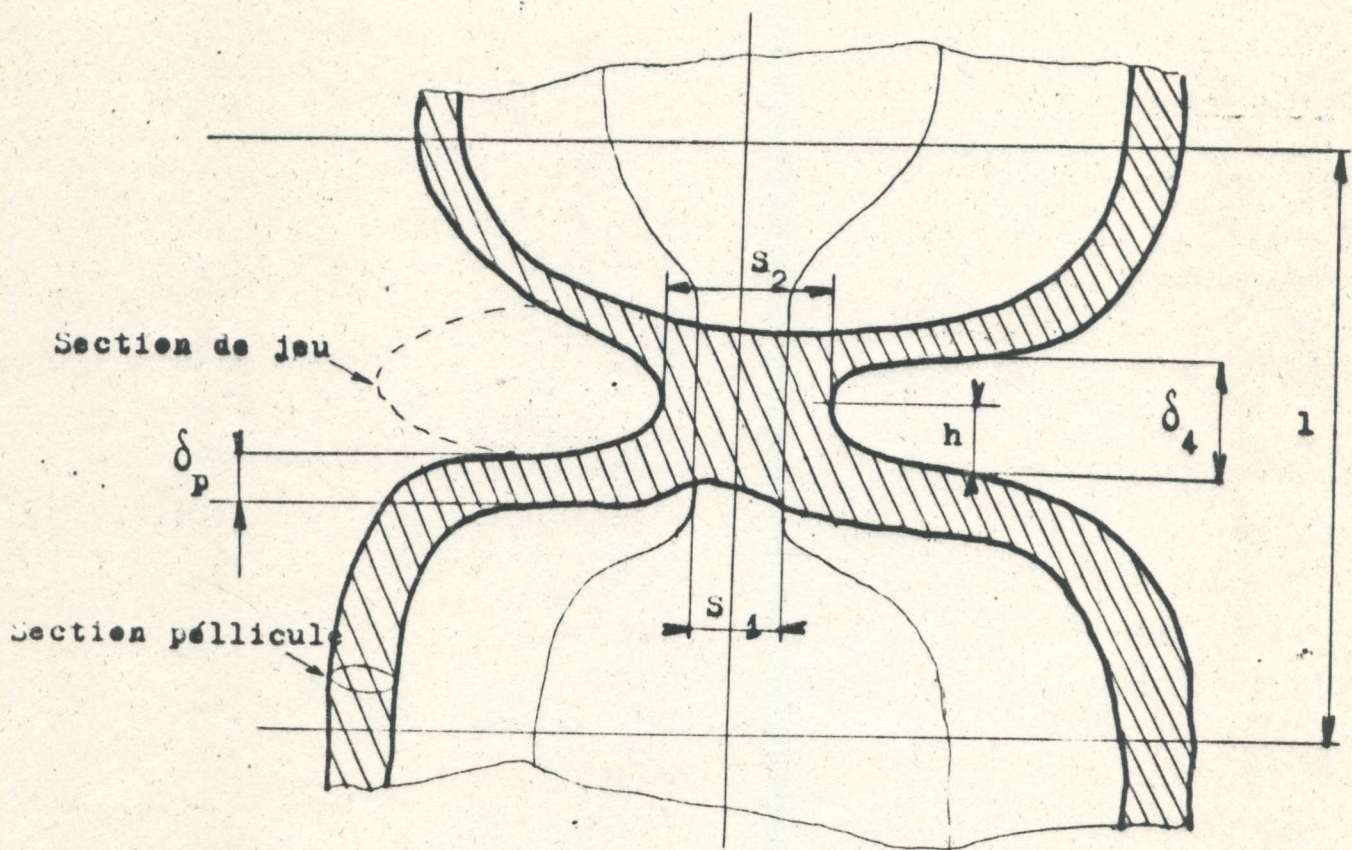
Pent métallique entre deux surfaces de contact.
